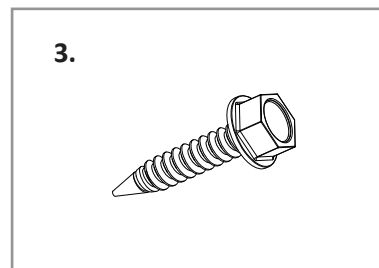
Fig. III Onderdelen / Parts / Teile / Pièces / Partes / Детали
